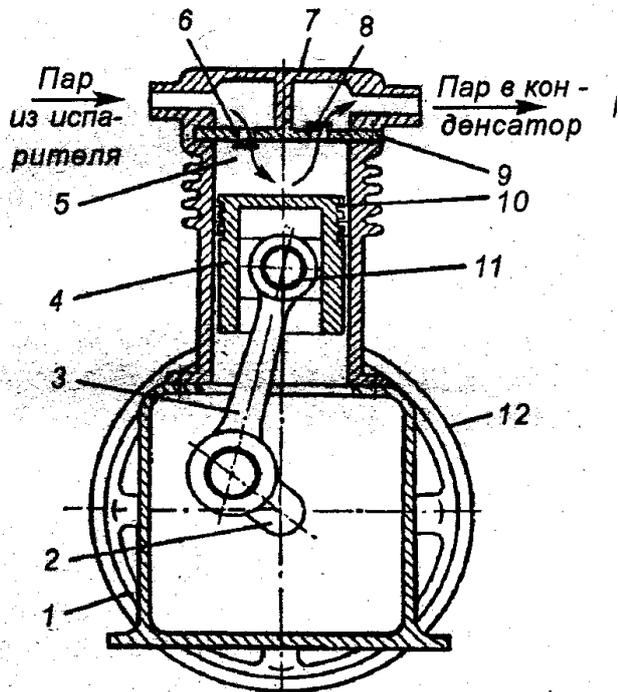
Схема одноступенчатого непрямоточного компрессора:
